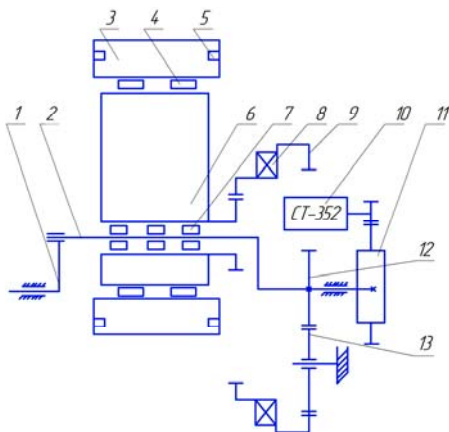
Кинематическая схема двигателя ПКРД-1:
